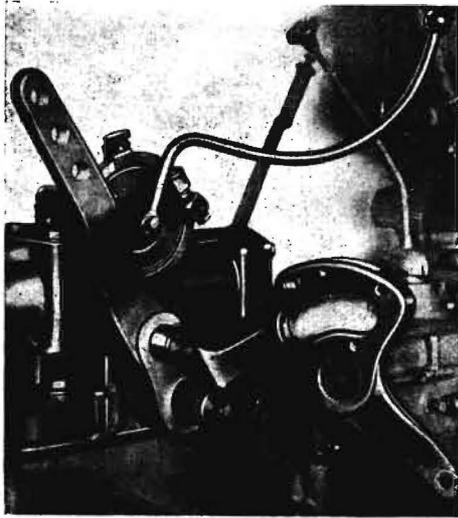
Hydraulischer Kraftheber (Regelzylinder) von Teves mit mechanischem Freigang
